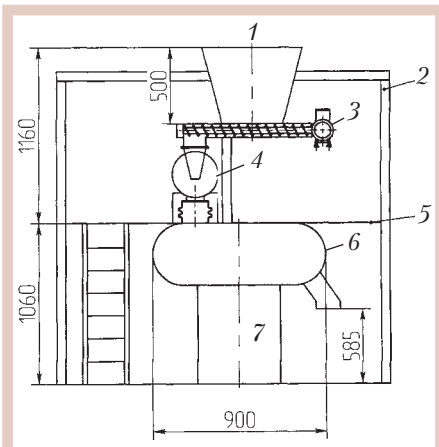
Схема комплекса оборудования для получения мелкодисперсных смесей для обсыпки тортов: 1 – бункер (емкость 0,1 м³); 2 – ограждение; 3 – питатель шнековый ПШ-0,1; 4 – мельница МН-0,25; 5 – настил; 6 – смеситель СМВ-0,1; 7 – привод
